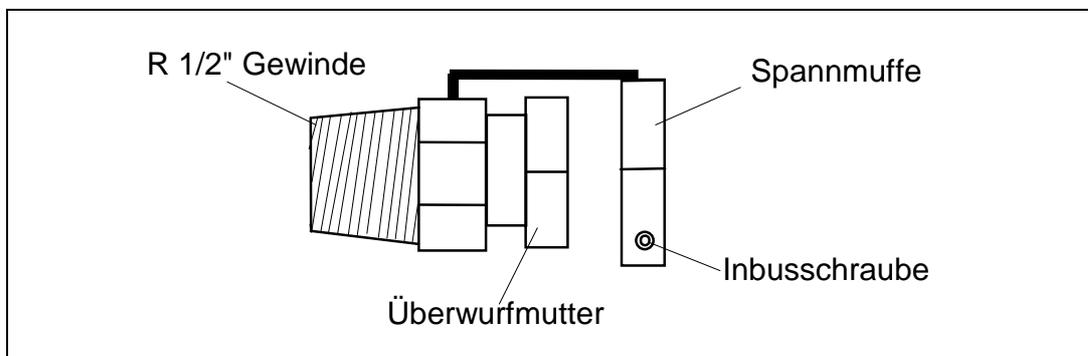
Klemmringverschraubung mit angeschweißter Spannmuffe
